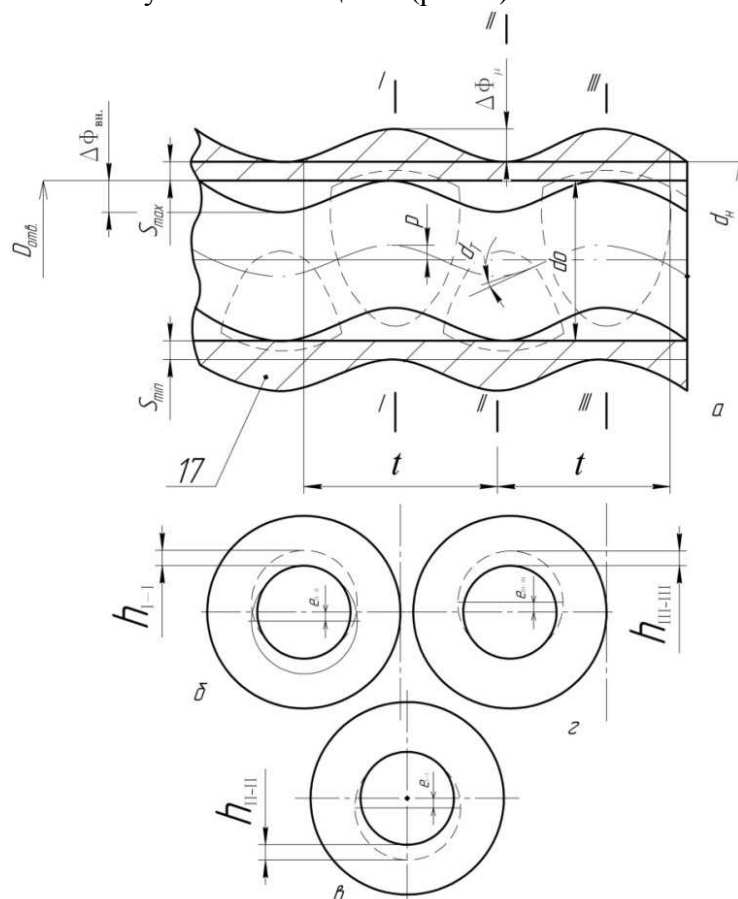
Геометрическая модель длинномерной трубной заготовки
